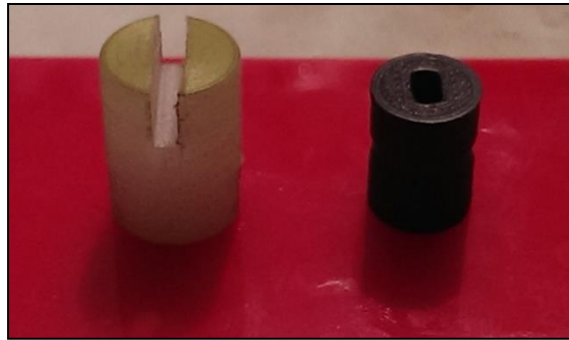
Izquierda: primer diseño acople; derecha: diseño final
